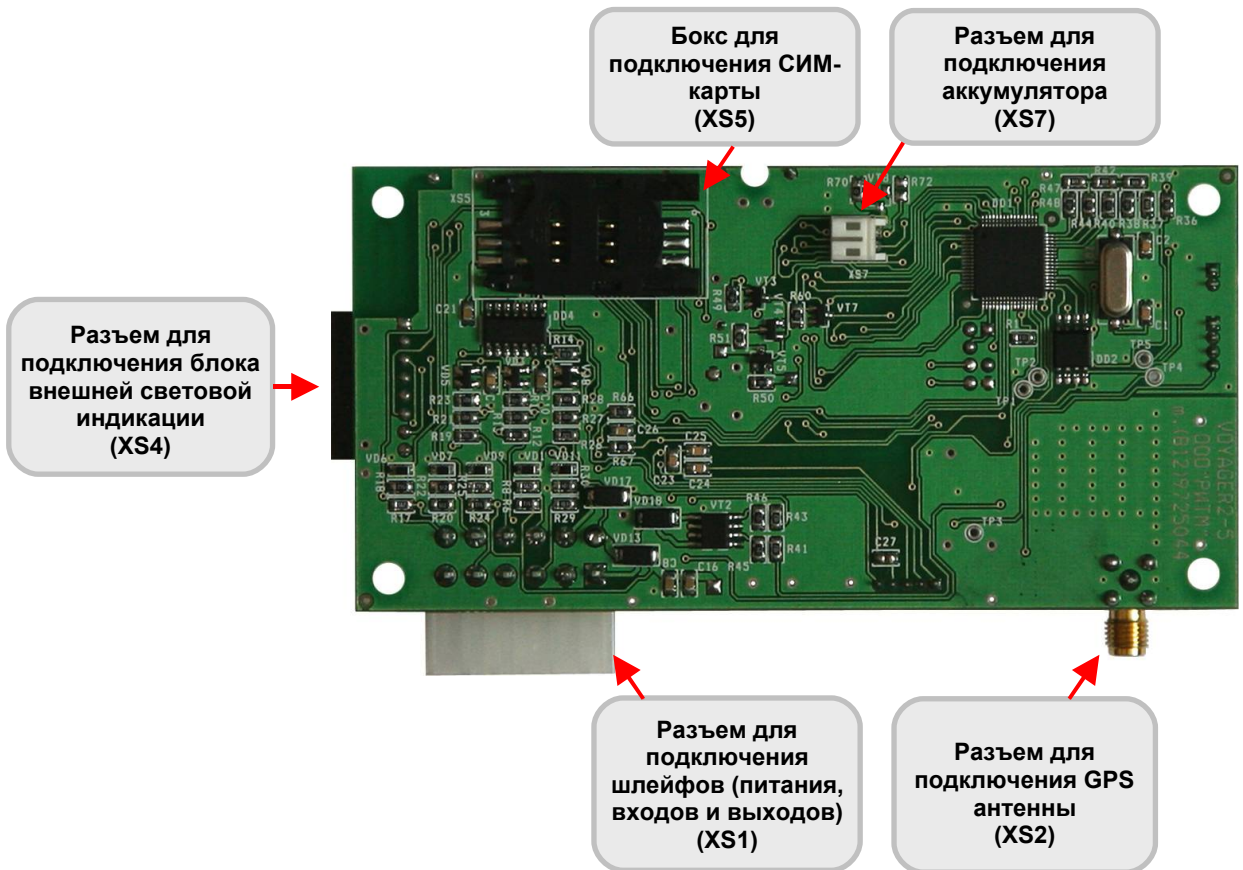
Разъемы объектового прибора «Вояджера» (новый корпус). Вид снизу.
